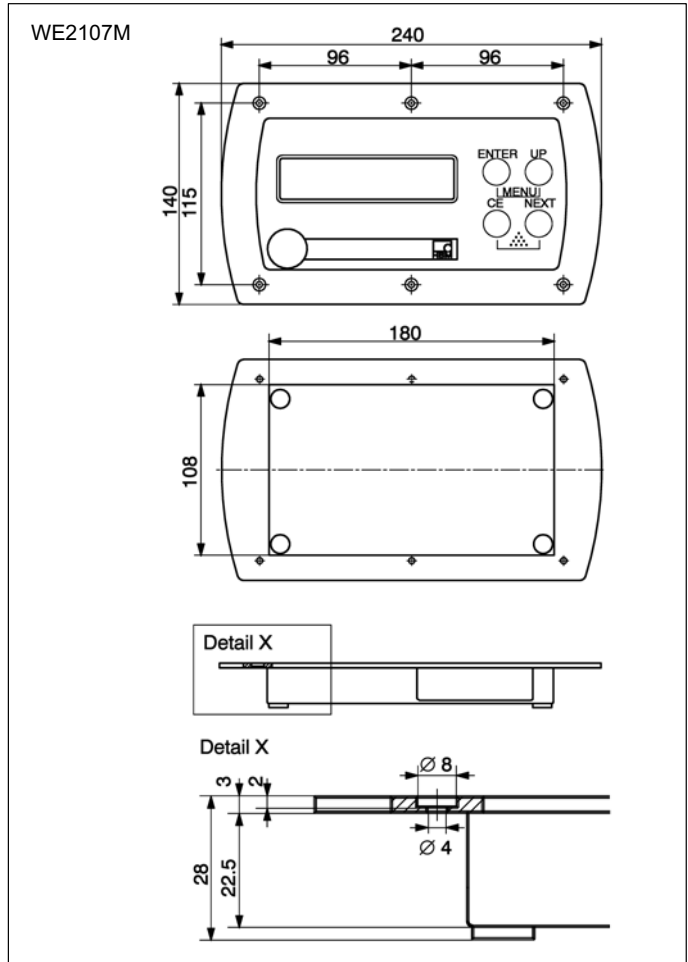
Dimensions du WE2107M (face avant en aluminium)
